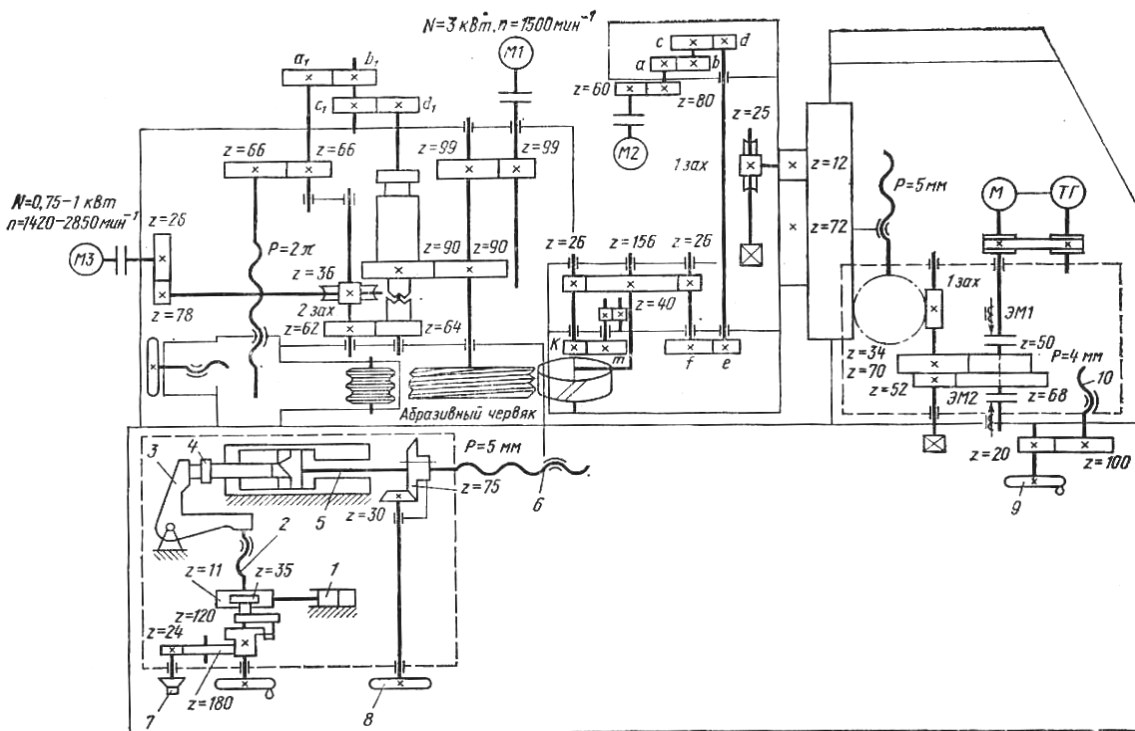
Кинематическая схема зубошлифовального станка модели 5B833
